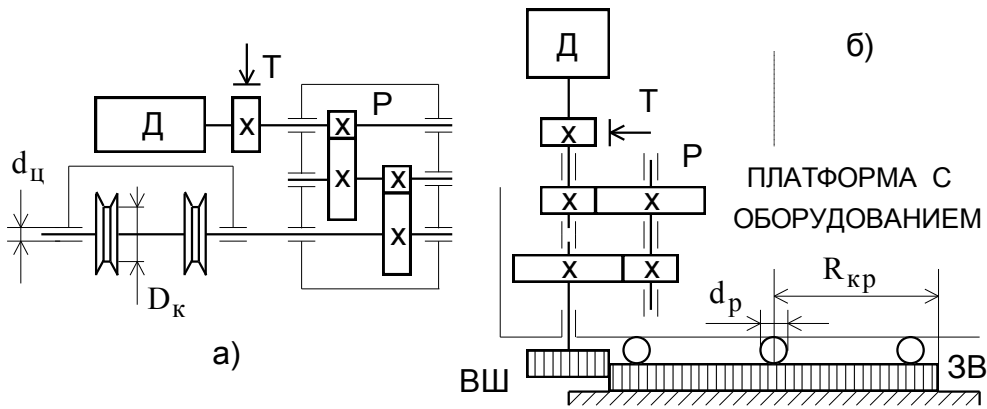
Кинематическая схема механизма передвижения (а) и поворота (б). Д - двигатель, Т - тормоз, Р - редуктор, ВШ - ведущая шестерня, ЗВ - зубчатый венец,  $D_k$  - диаметр колеса,  $d_{\text{ц}}$  - диаметр цапф (подшипников) колес,  $R_{\text{кр}}$  - радиус роликового круга,  $d_p$  - диаметр роликов (в случае опорных тележек - диаметр их колес)
